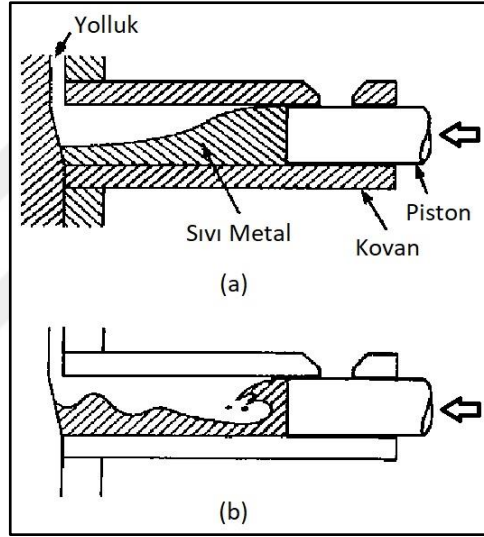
Soğuk kamaralı yüksek basınçlı döküm makinesi [14].
